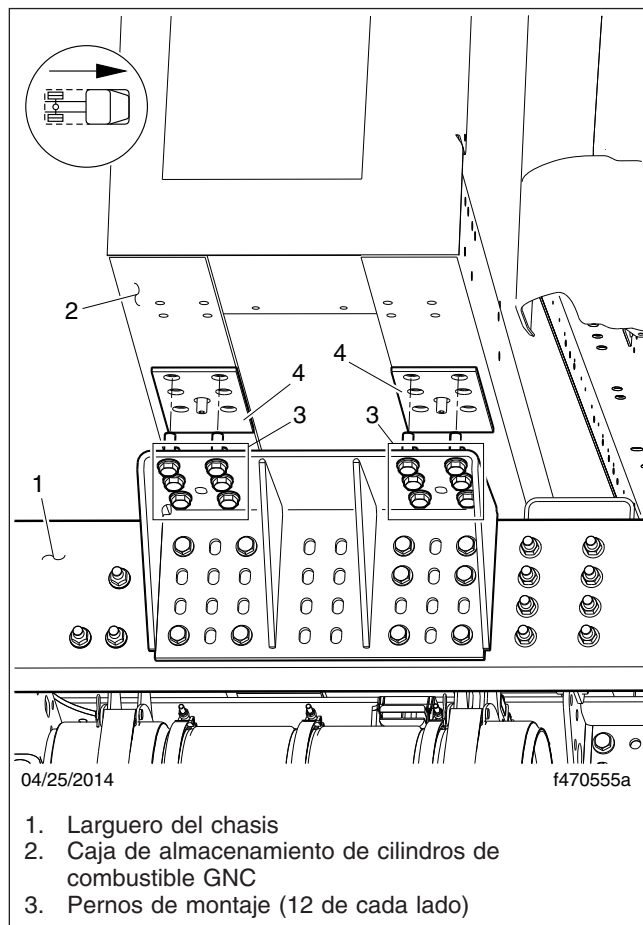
, Soporte de montaje de la caja de almacenamiento de cilindros de combustible (lado del pasajero)
